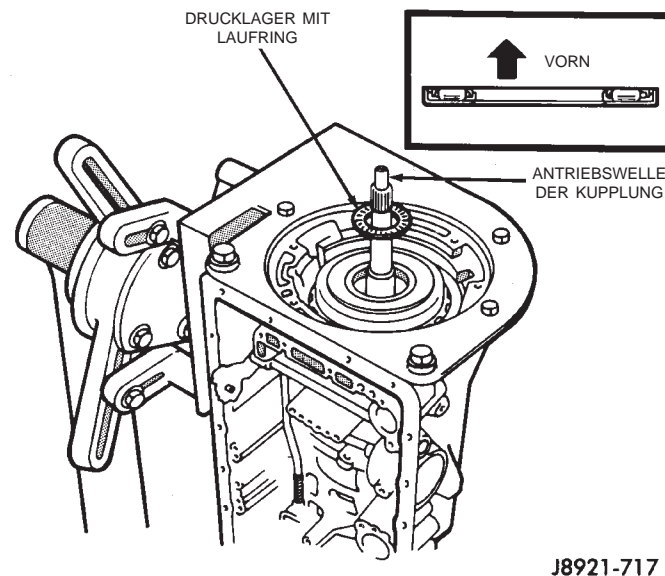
Anlaufring für Planetenradsatz montieren
